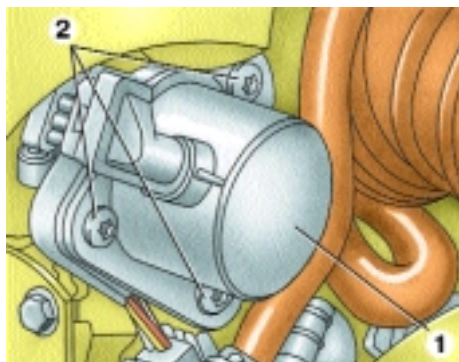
Крепление датчика порядкового номера цилиндра к головке блока двигателя F3R 272: 1 – датчик порядкового номера цилиндра; 2 – болты крепления
